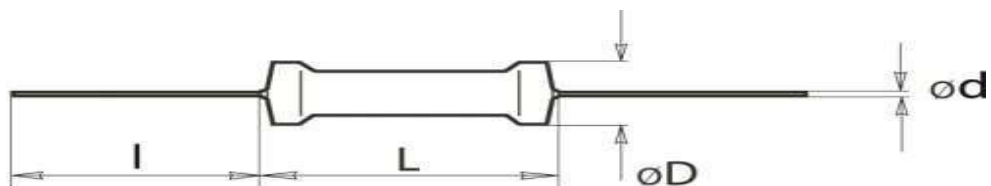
Зовнішній вигляд резистора постійного резистора C2-33.
